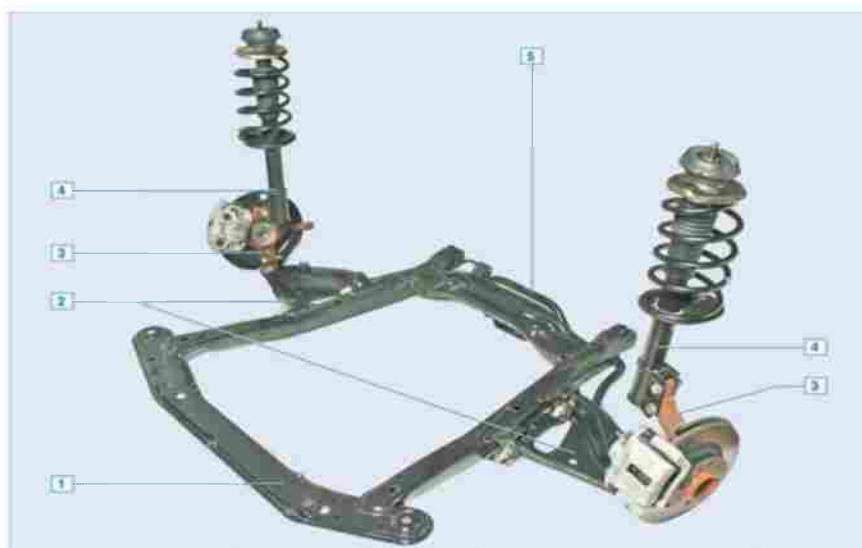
Передняя подвеска: 1 - подрамник; 2 - рычаг подвески с сайлент-блоками и шаровой опорой; 3 - поворотный кулак со ступицей и подшипником; 4 - амортизаторная стойка; 5 - штанга стабилизатора поперечной устойчивости.
